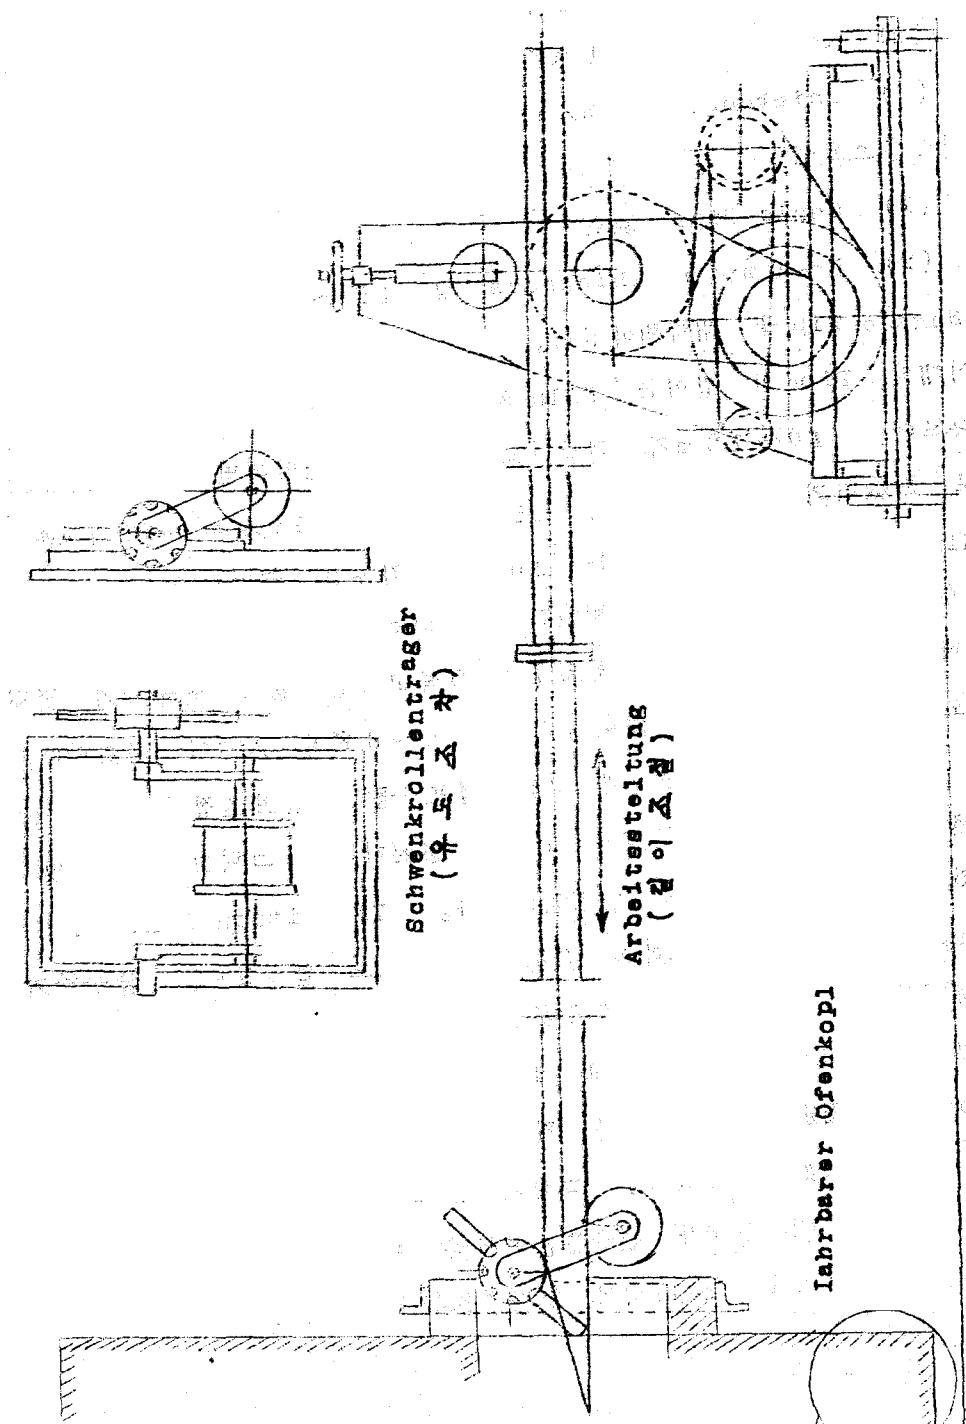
Bruchmaschinezum Entfernen von Schleckenringen in
